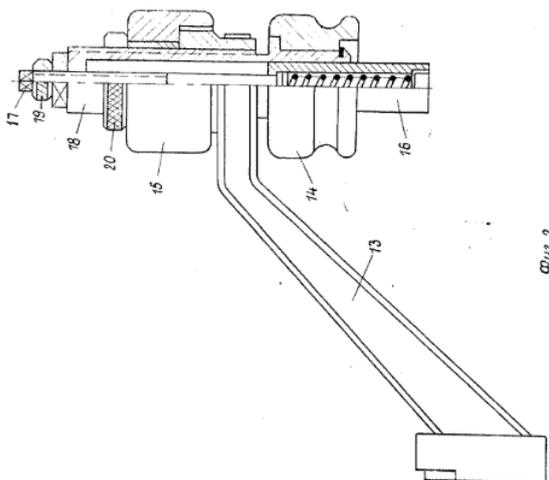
Приспособление для снятия замочного кольца колес автомобиля
